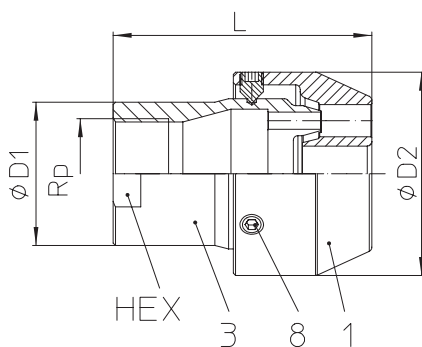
2 mit Innengewinde (Rp 1 - Rp 1 1/2)
